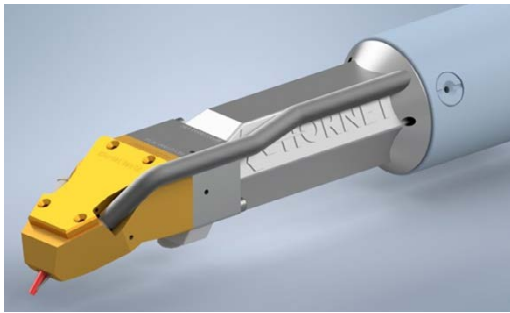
Laser-Innenbeschichtungen mit Fülldraht
